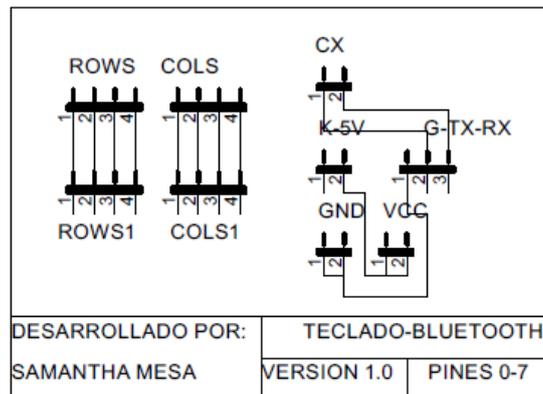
DISEÑO PLACAS TECLADO Y BLUETOOTH
